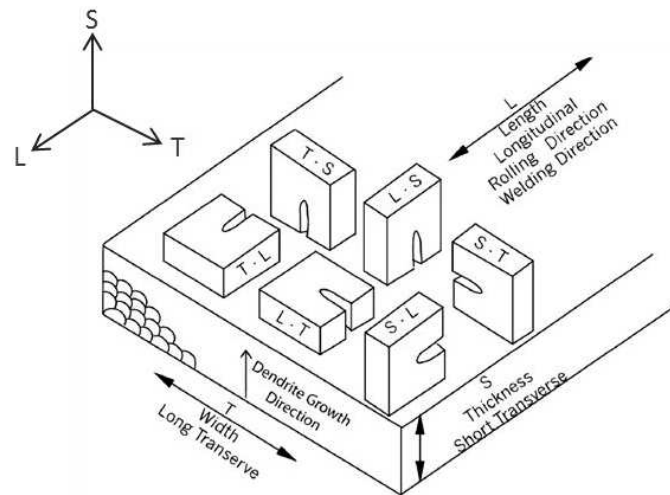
Sens de prélèvement des éprouvettes CT suivant la direction de soudage L, la largeur de la soudure T et l'épaisseur de la soudure S [White2005]
